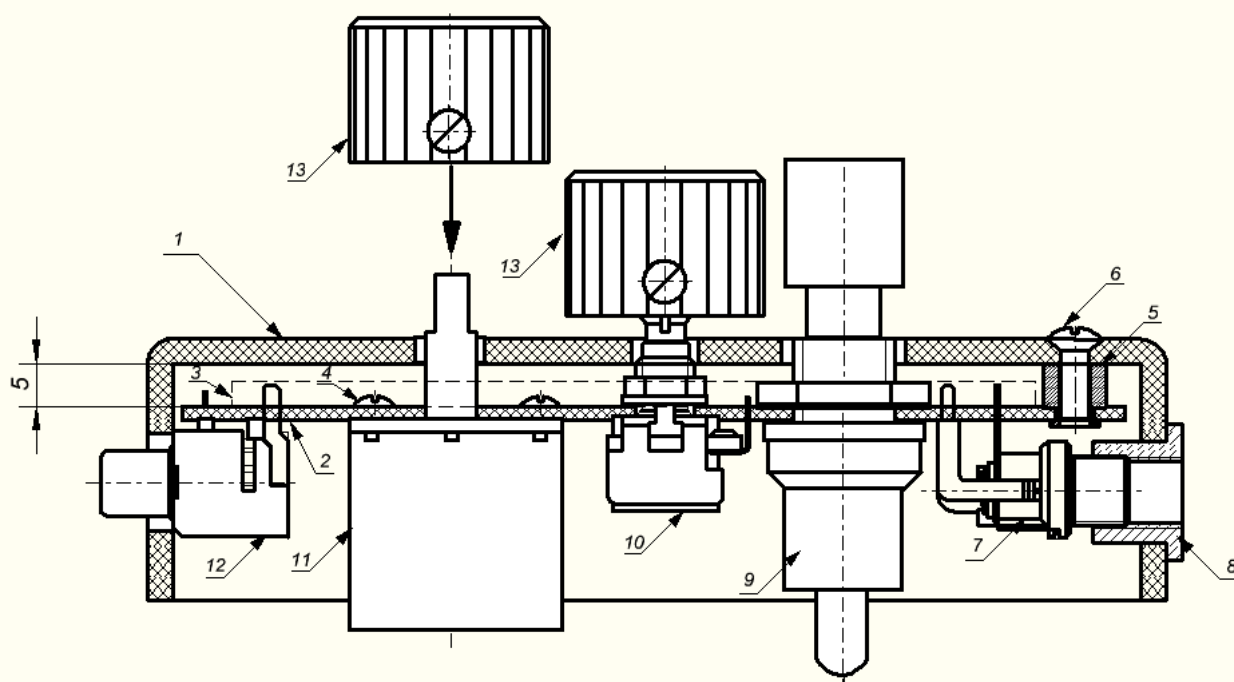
Схема варианта монтажа платы на крышке корпуса G386/278 фирмы Gainta: 1 – крышка корпуса; 2 – печатная плата; 3 – место монтажа ПМИ; 4 – винт для крепления КПЕ к печатной плате; 5 – втулка резьбовая для крепления печатной плате; 6 – винт; 7 – гнездо питания; 8 – втулка резьбовая для фиксации гнезда питания; 9 – кнопка включения питания; 10 – переменный резистор; 11 – переменный конденсатор; 12 – ВЧ гнездо; 13 - ручка
